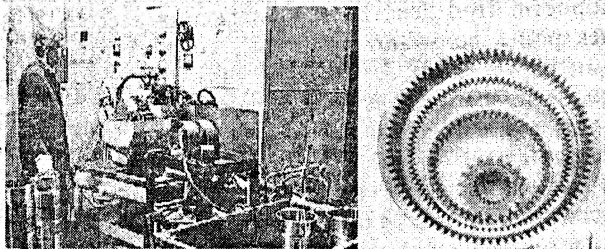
Индукционная установка для закалки шестерен колесной передачи МАЗ - а и шестерни - б, подвергаемые поверхностной индукционной закалке.
